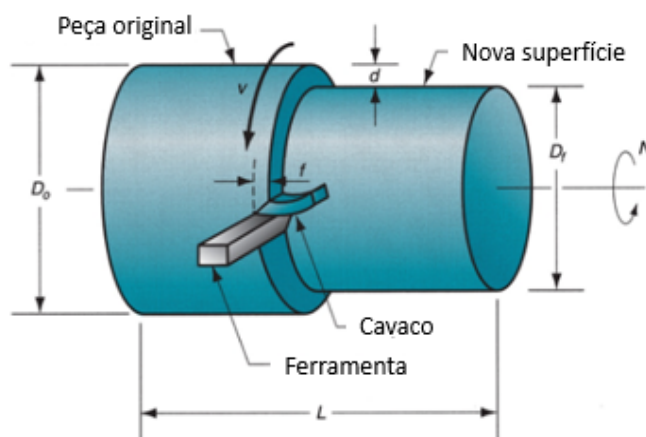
Operação de torneamento (GROOVER, 2014)
